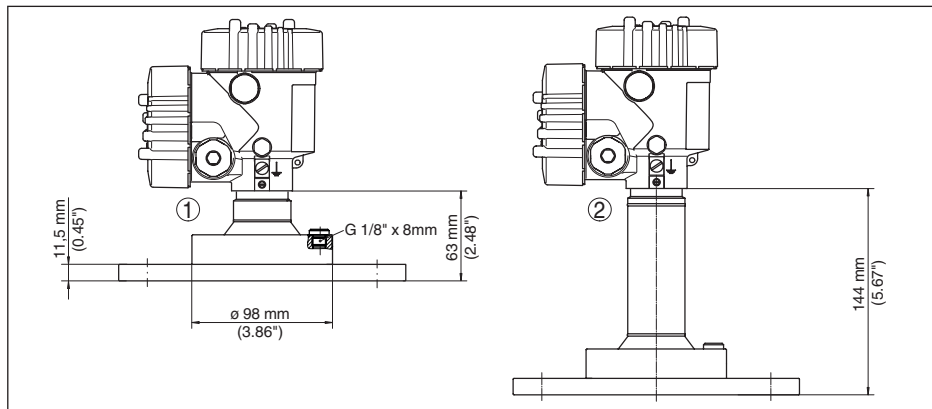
VEGAPULS 6X, flange com antena lentiforme (espessura da flange, vide desenho, tamanho do flange conforme DIN, ASME, JIS)
